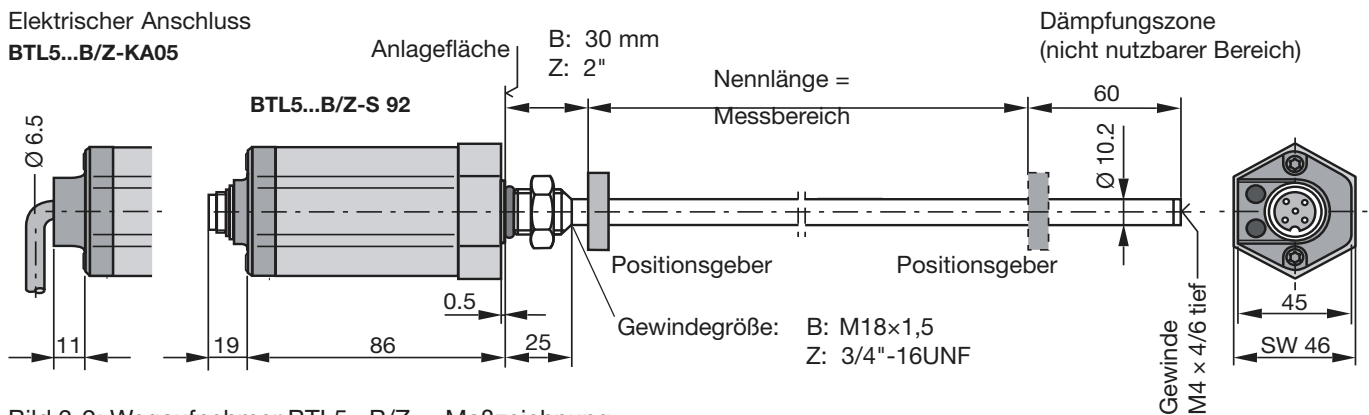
Wegaufnehmer BTL5...B/Z..., Maßzeichnung
